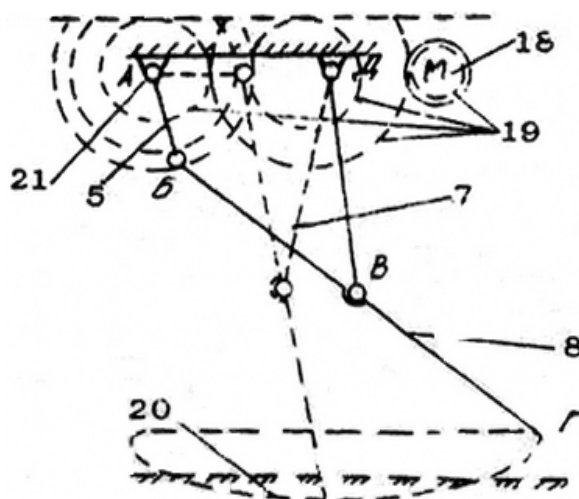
Кинематическая схема направляющего механизма с приводом
